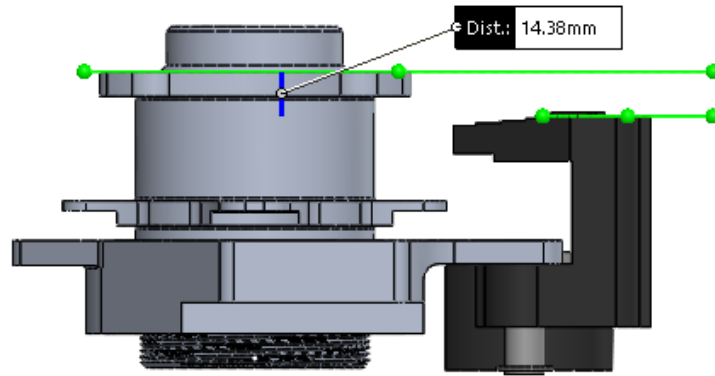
Detalhe para a distância entre o plano de fixação da roda e o plano mais externo da pinça de freio.
